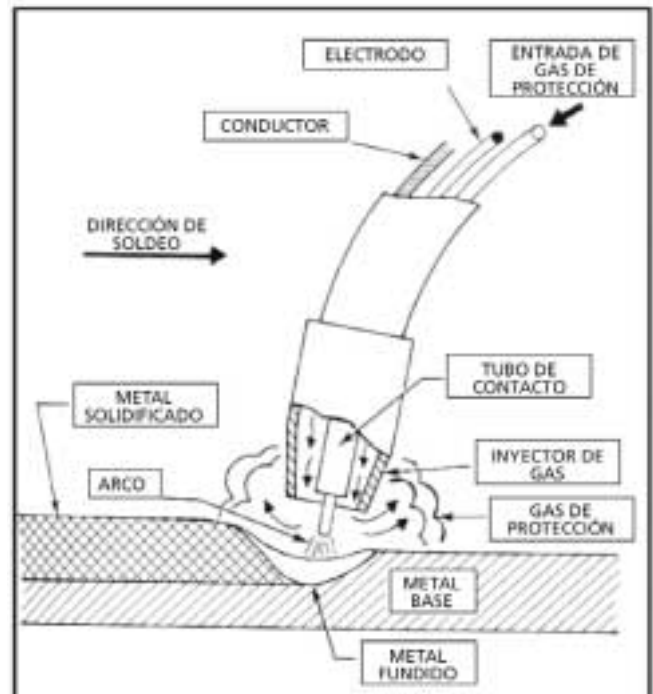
Proceso de soldadura por arco con gas protector y electrodo consumible
